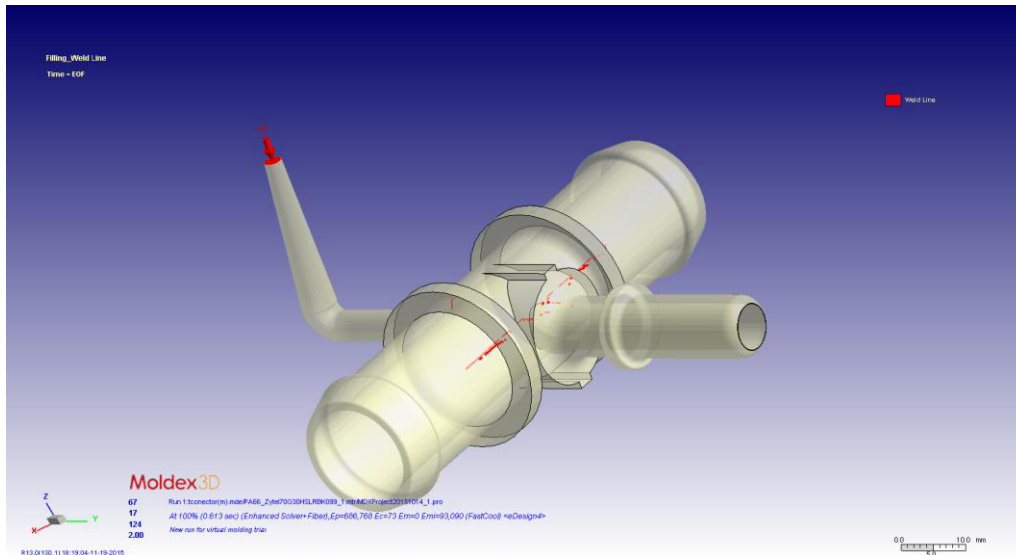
Localização das linhas de soldadura das moldações do Projeto C
